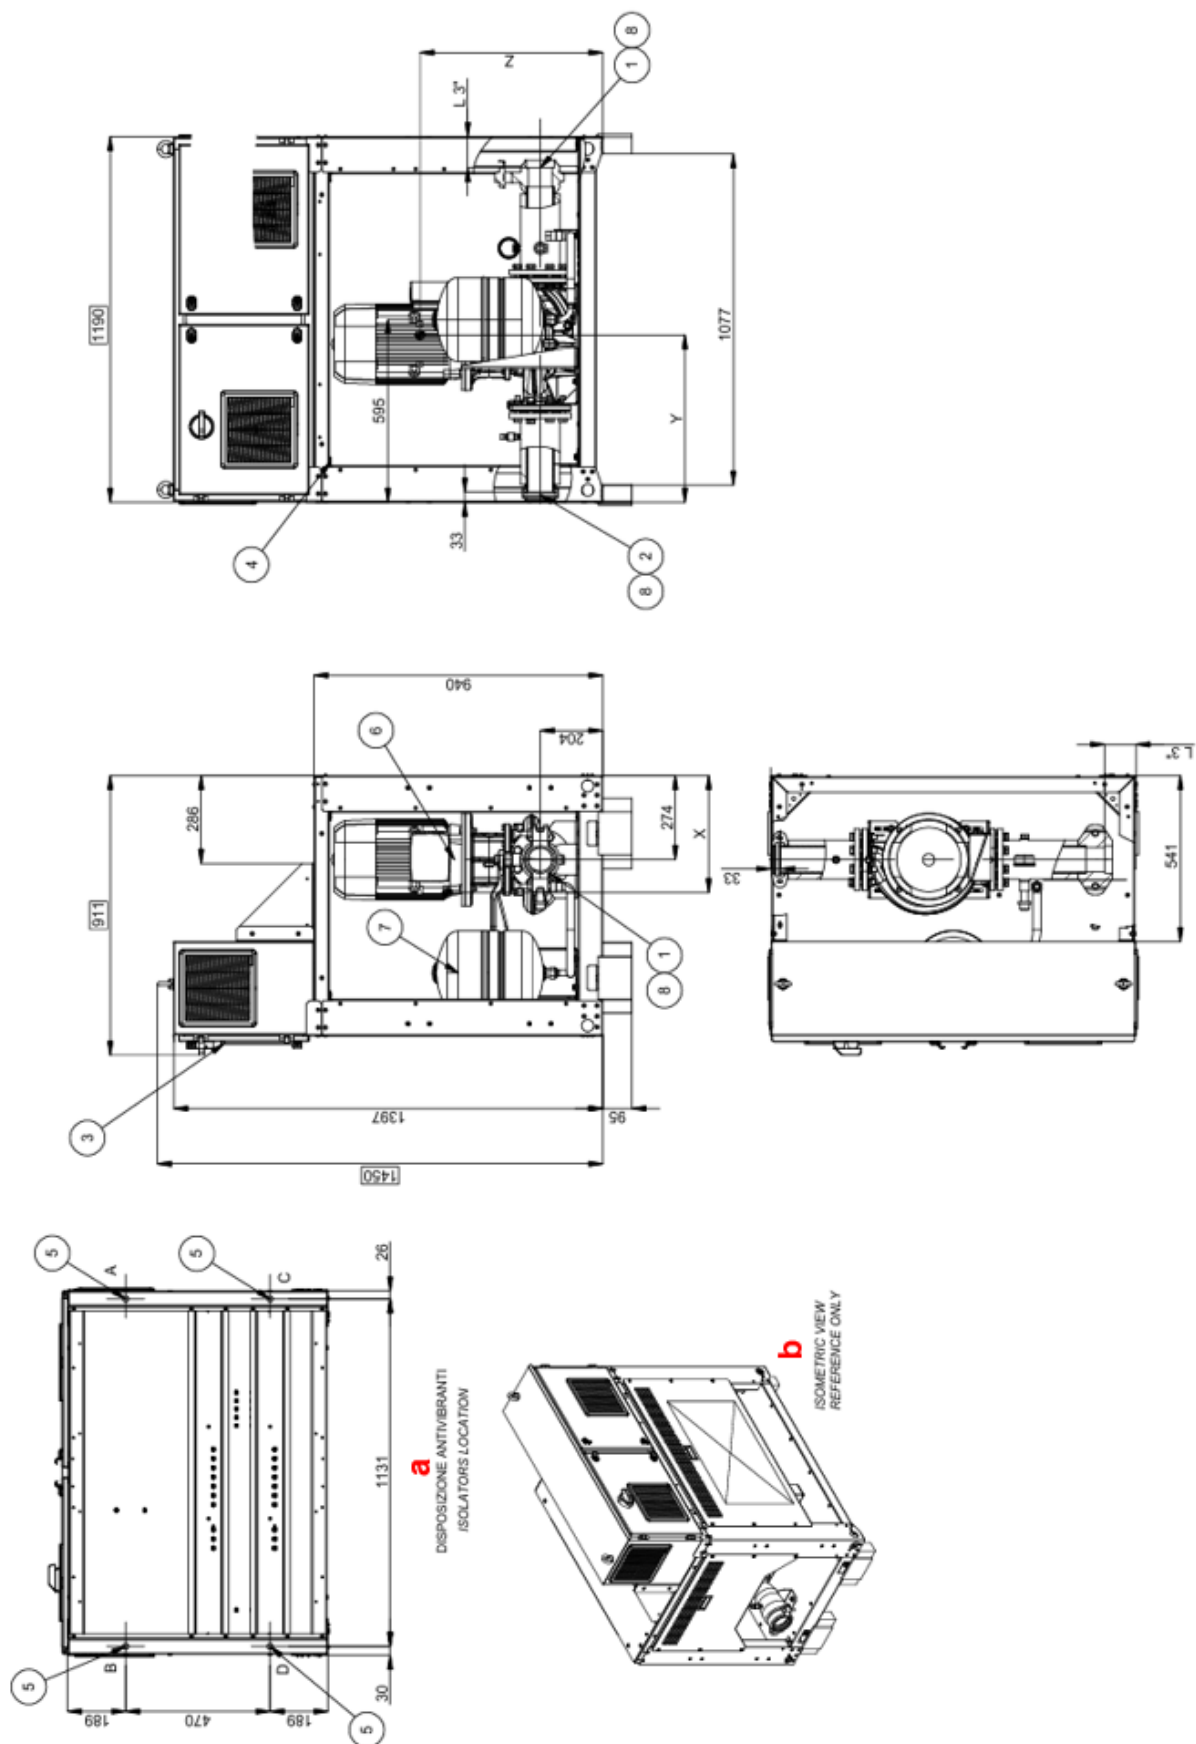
Maßzeichnungen – Pumpenmodule
